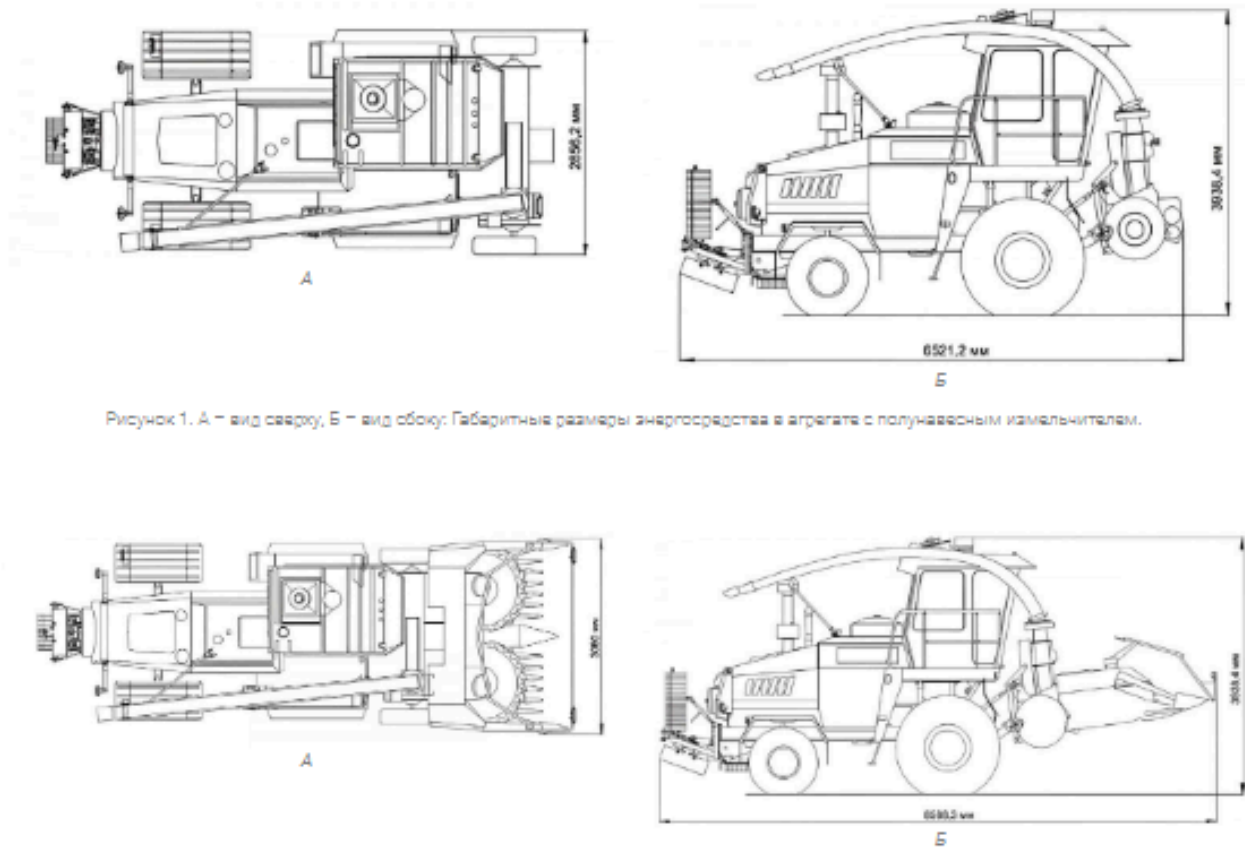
А – вид сверху, Б – вид сбоку: Габаритные размеры энергосредств в агрегате с полуавтоматическим измельчителем.
